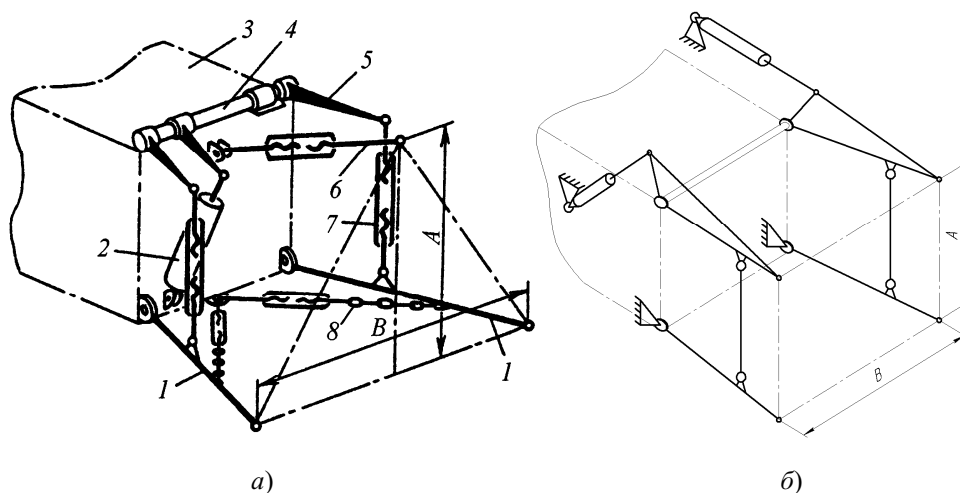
Схемы для трехточечного (а) механизма навески трактора и четырехточечного (б) механизма навески самоходного измельчителя: 1, 6 – тяги; 2 – гидроцилиндр; 3 – трактор (рама); 4 – вал; 5 – поворотный рычаг; 7 – раскос
